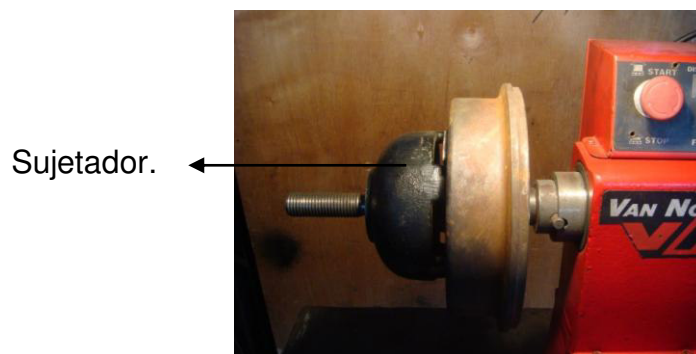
Conjunto de sujetador, tambor y adaptadores.
